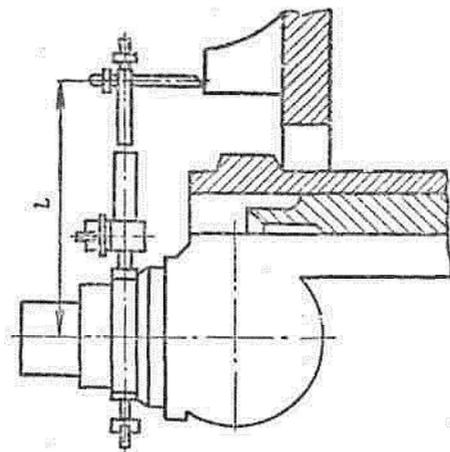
Выставка углового положения балансира приспособлением ВП1
